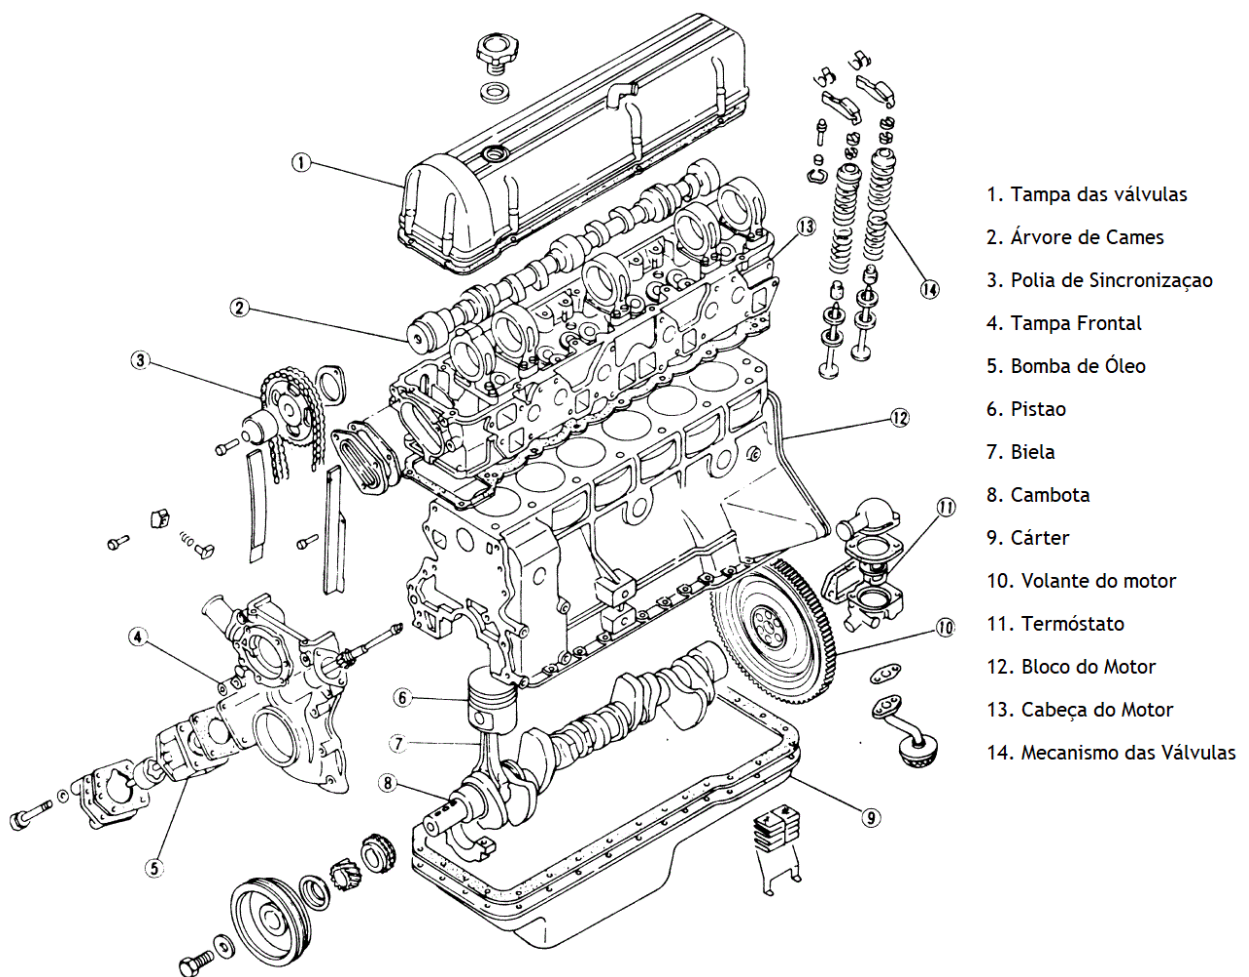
, Imagem explodida de um Motor de Combustão Interna. [Extraído de <https://tailoutsx.files.wordpress.com/2010/02/exploded20l28.gif>]
